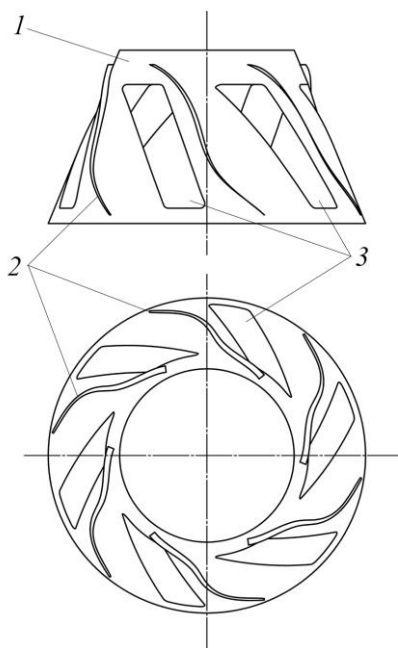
Загальний вигляд фрези: 1 – корпус; 2 – різальні елементи; 3 – отвори
